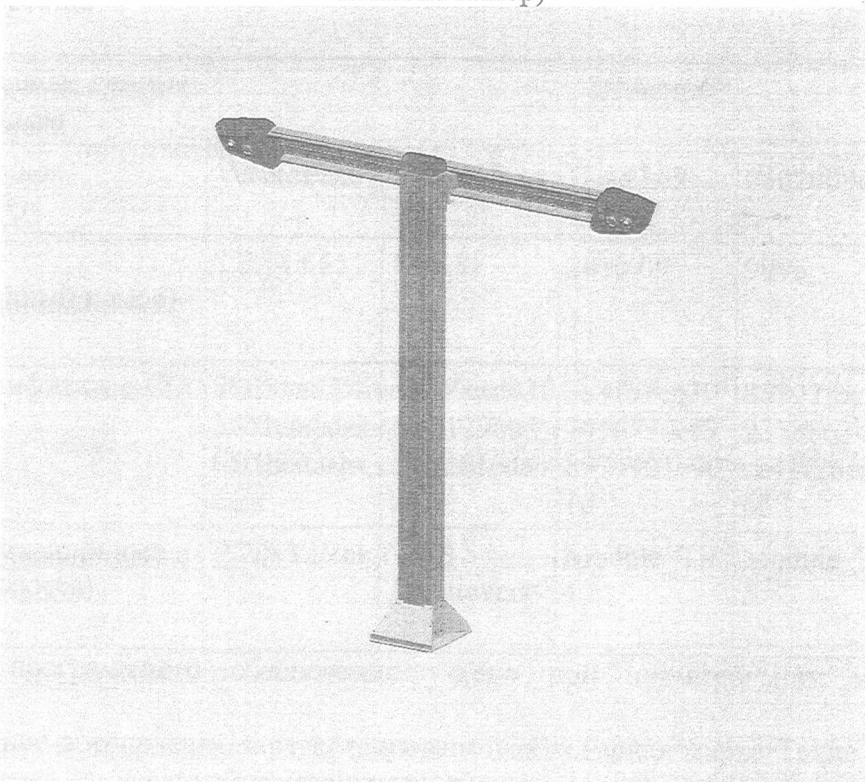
модификации 7212, 7214 (Корпус видеокамер тип Т, оборудованный механизмом подъема камер)
